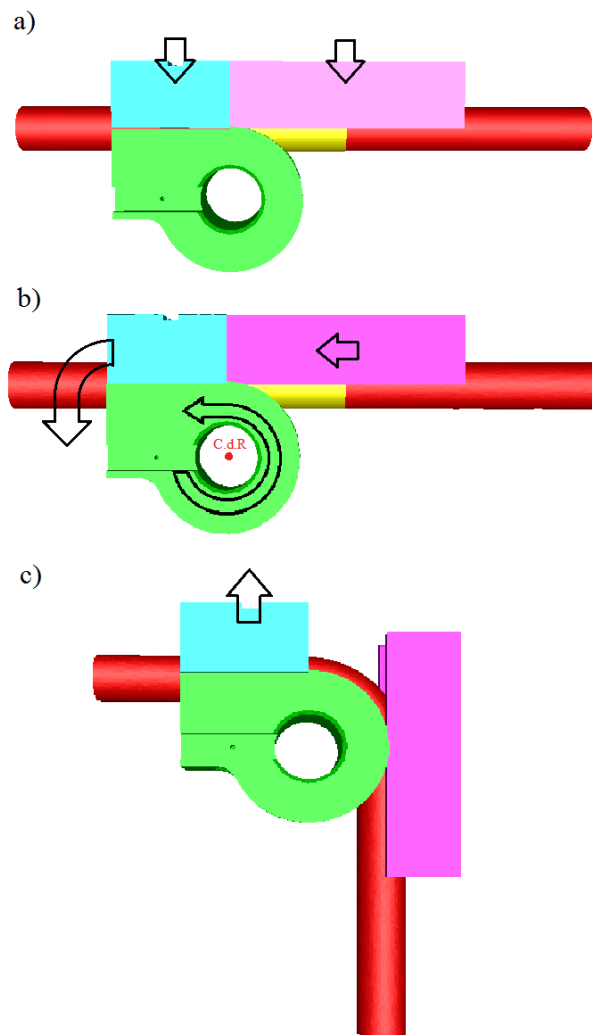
a) step di chiusura; b) step di piega con evidenziato il Centro di Rotazione (C.d.R) di bending tool e clamp die; c) step di ritorno.
